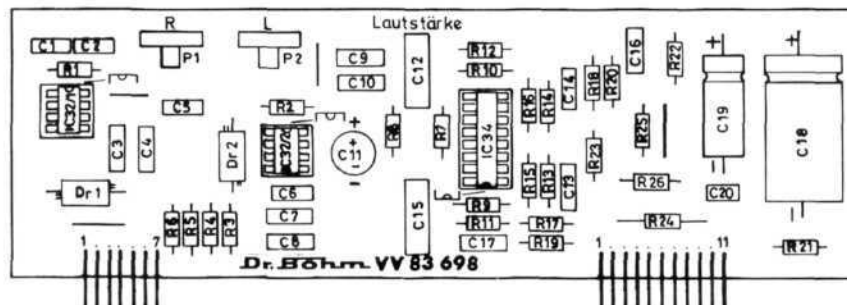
Positionsnummernplan Lautstärke-Modul Platine VV 83 698
